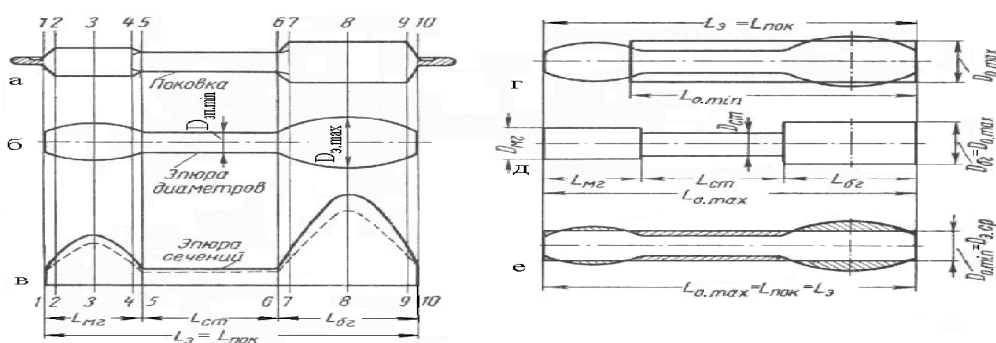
Неравномерность деформации при осадке и варианты заготовок для штамповки: а – поковка; б – эпюры диаметров; в – эпюры сечений; г – заготовка требующая протяжки, д – заготовка фасонная, е – заготовка требующая подкатки [1,3]
